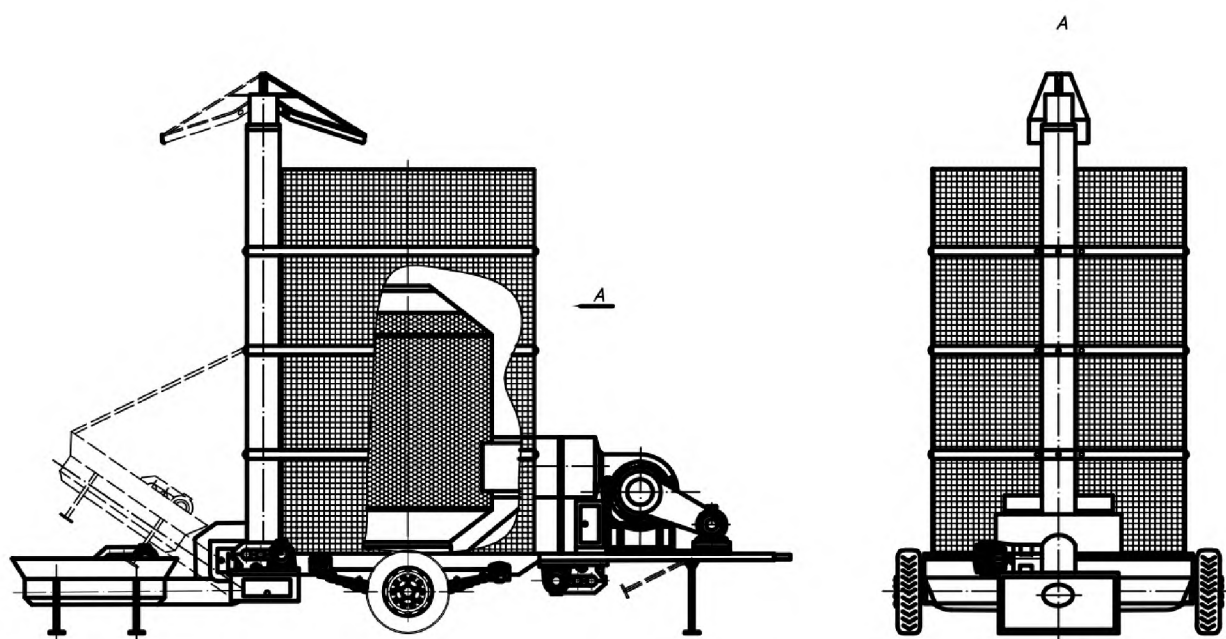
Загальний вигляд мобільної зерносушарки для сорго
